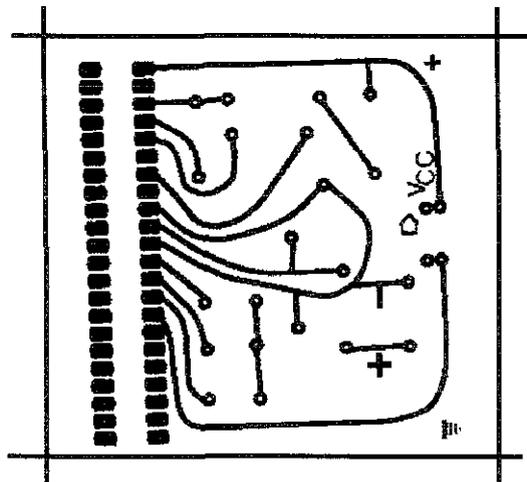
Dibujo del Circuito Impreso del Medidor de Voltaje Directo en el Módulo transmisor Base lado de las pistas.
